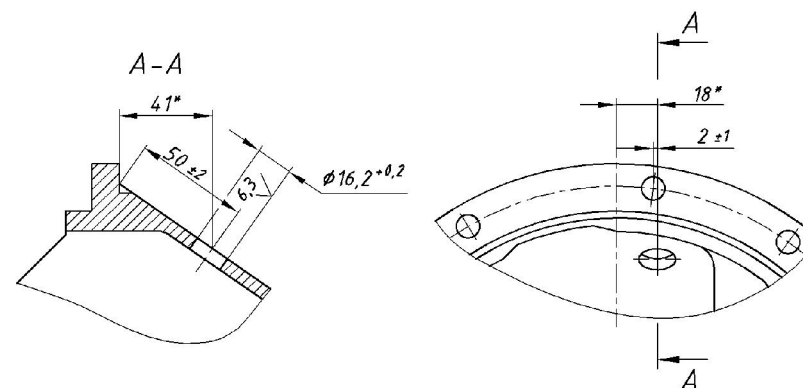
в Эскиз доработки картера редуктора 3302-2402013 для заднего моста
